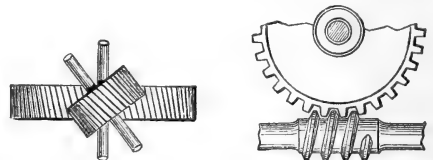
Schraubenräder. Fig. 5. Schraube ohne Ende.
